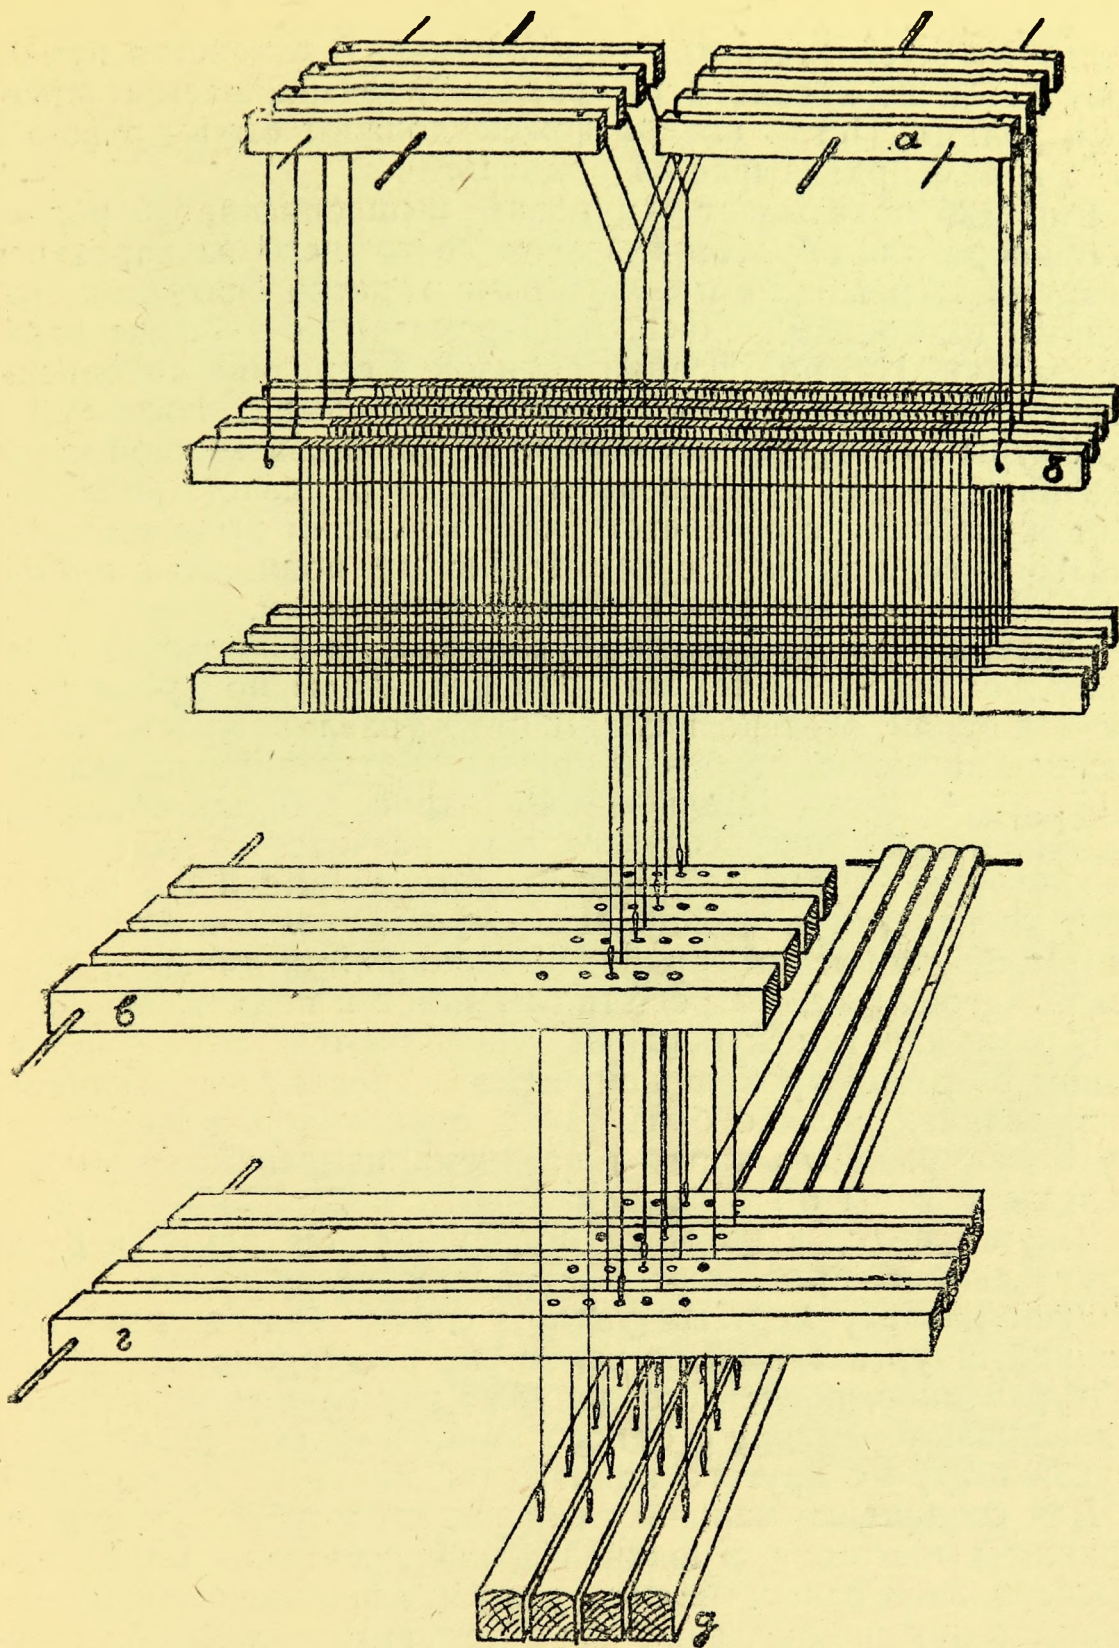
Соединение каретки с ремизками, рычагами и под-
